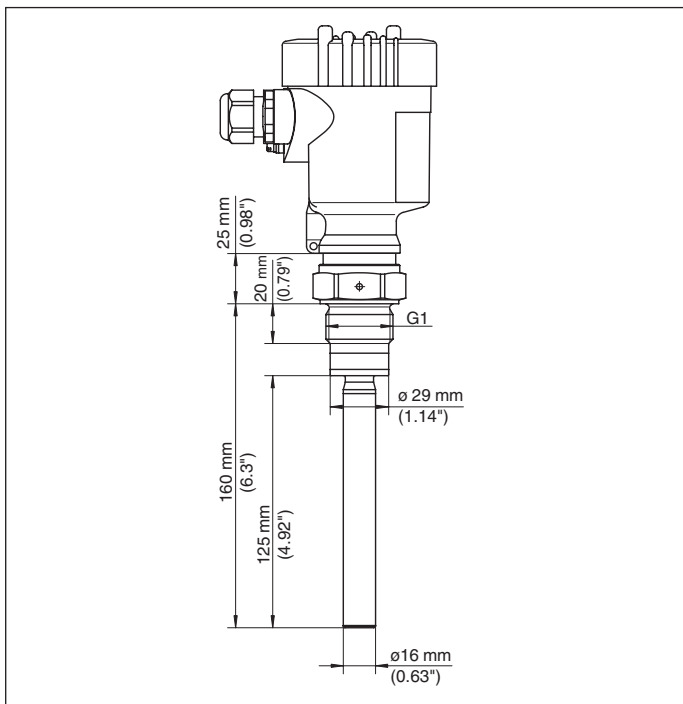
VEGA VIB 61 - резьбовое исполнение G1
